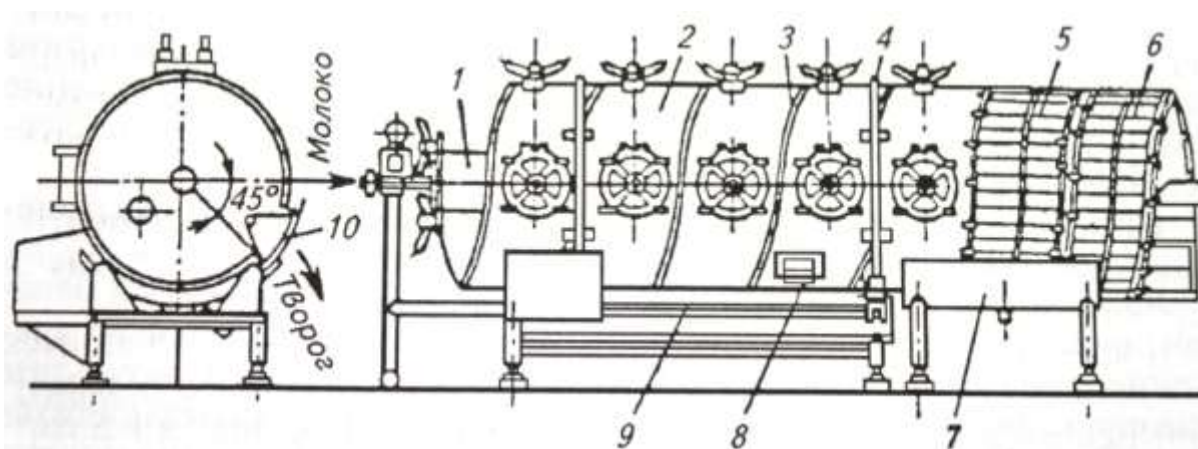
Многосекционный творогоизготовитель непрерывного действия:
